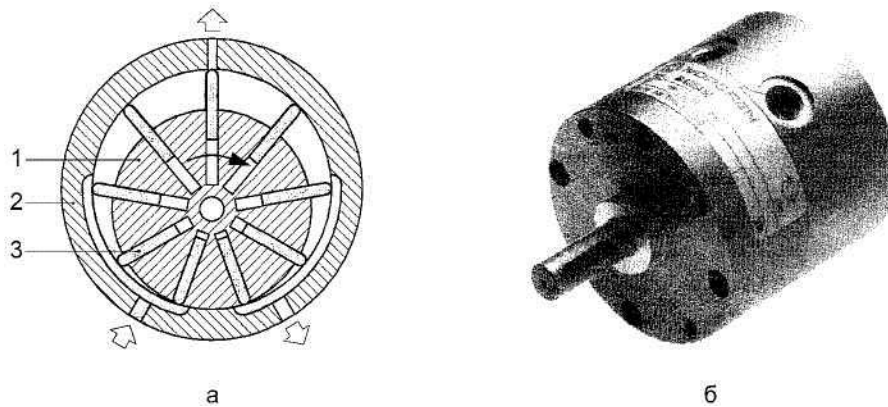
Ротаційний (шиберний) пневмомотор:
